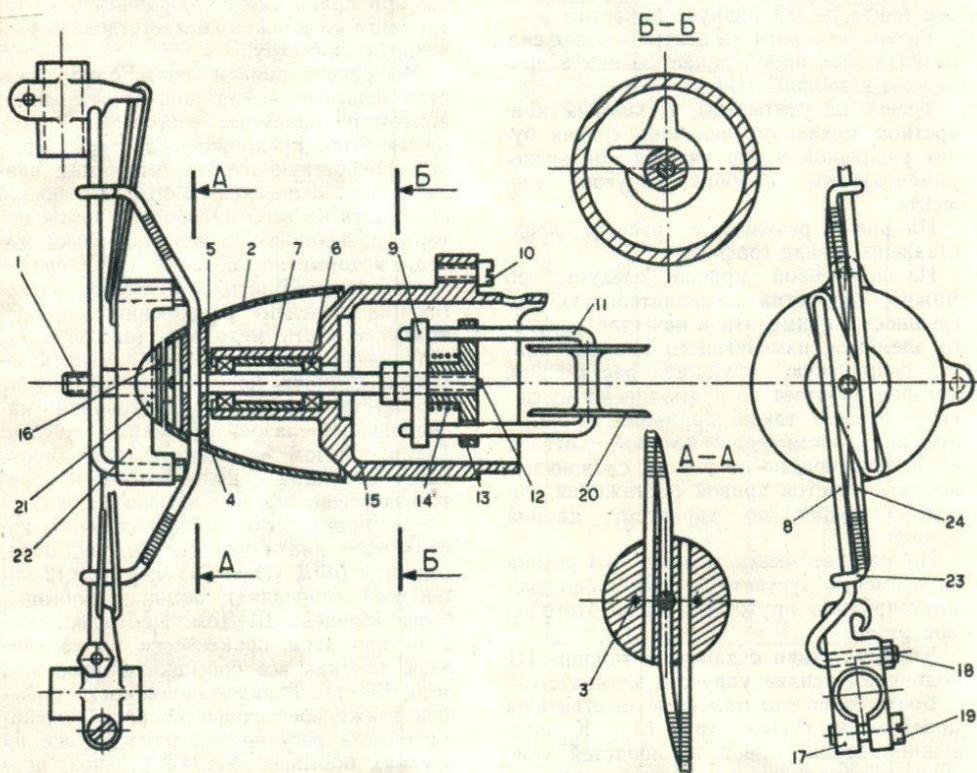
Винт изменяемого диаметра рычажной конструкции. 1 — вал; 2 — кон; 3 — штифт; 4 — диск; 5 — пластина; 6 — шарикоподшипник; 7 — распорная втулка; 8 — синхронизатор; 9 — траверза; 10 — винт; 11 — скоба; 12 — упор; 13 — траверза; 14 — пружина; 15 — бобышка; 16 — пластина; 17 — хомут; 18 — гайка; 19 — винт; 20 — ролик; 21 — обтекатель; 22 — двуплечая качалка; 23 — направляющая; 24 — тяга.
